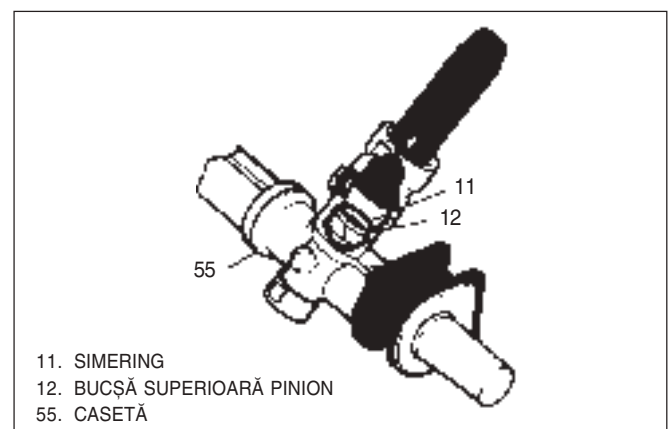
Montare simering ax pinion și bucsă superioară pinion
